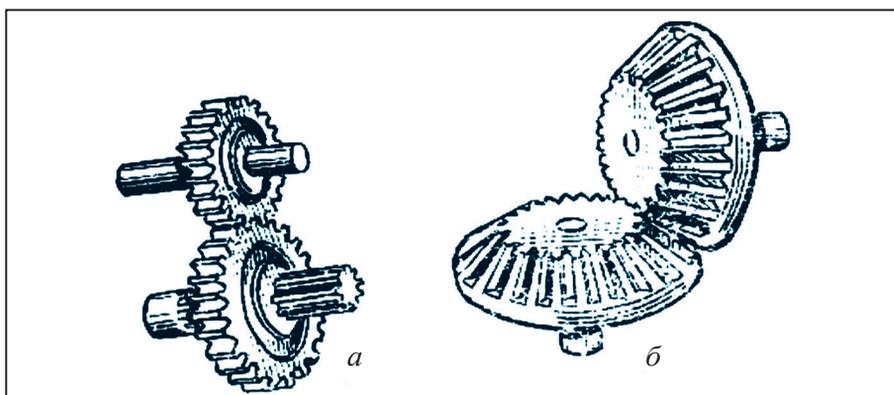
Цилиндрические (а) и конусообразные зубчатые (б) передачи.
